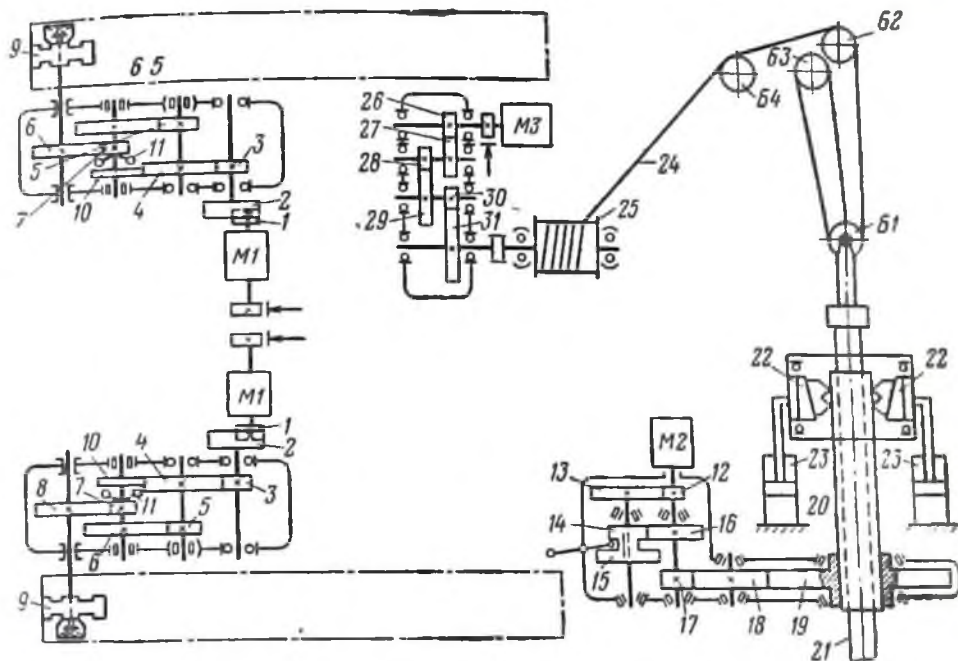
Кинематическая схема станка 2СВШ-200Н
